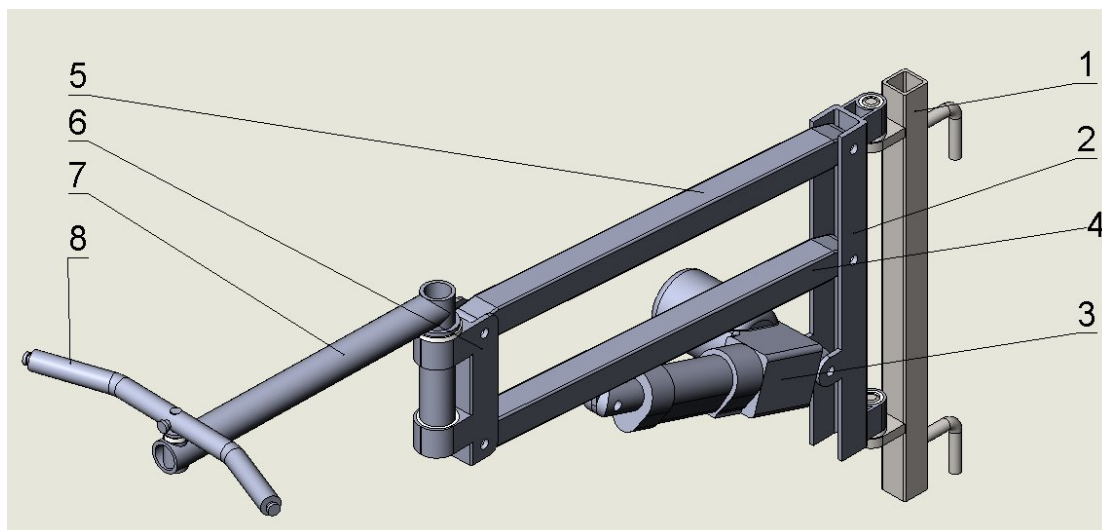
Загальний вид підйомника для людини з інвалідністю:
